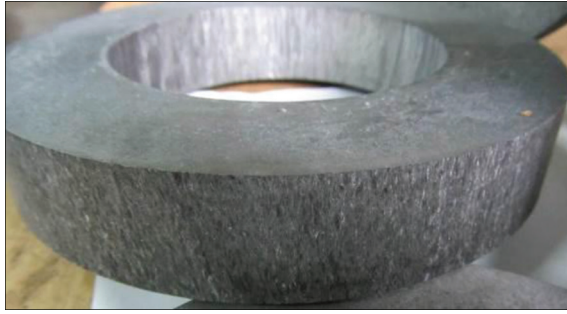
Макроструктура трубної заготовки $\varnothing 190/90$ мм із титанового сплаву ВТ14
